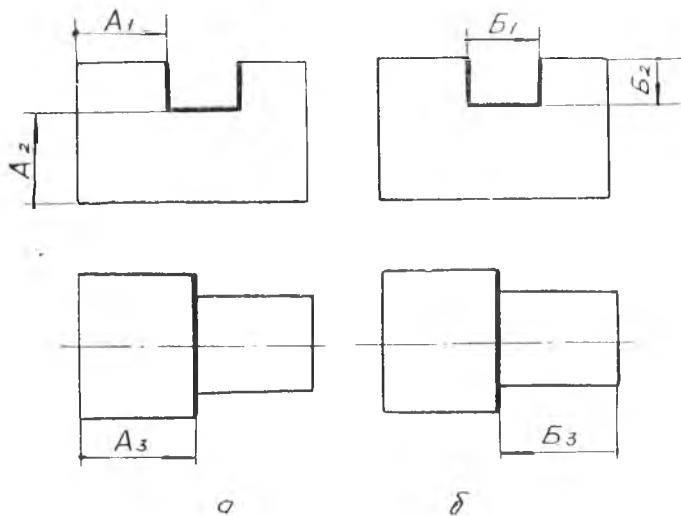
Схемы к выбору систем простановки допуска на операционный размер: *a* — по системе вала; *б* — по системе отверстия
